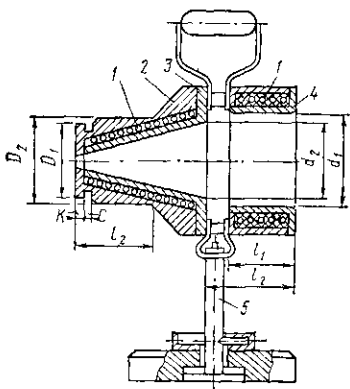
Приспособление для контактной раструбно-стыковой сварки труб и фасонных частей из ПНП, ПВХ и ПП
